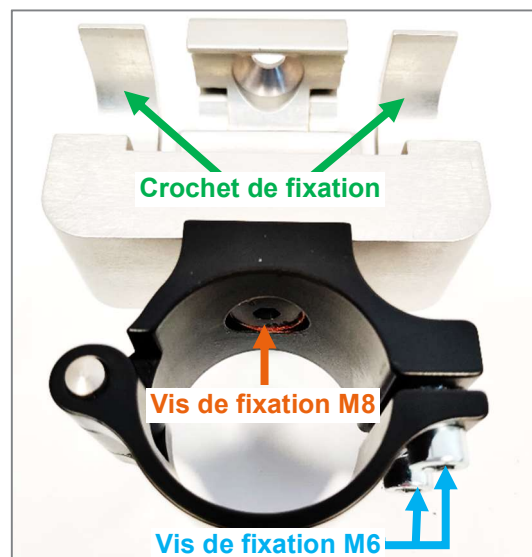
Vis de fixation M8 pour le réglage de la hauteur du clip de serrage
